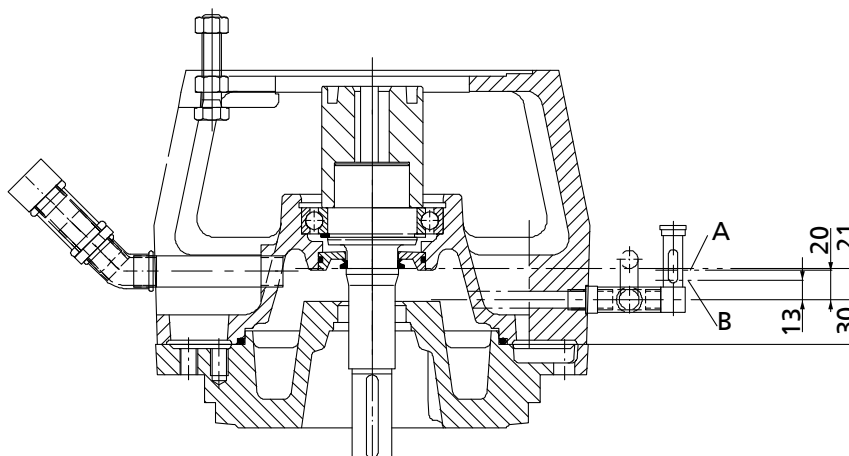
Naplnění olejové předkomory – horizontální instalace
